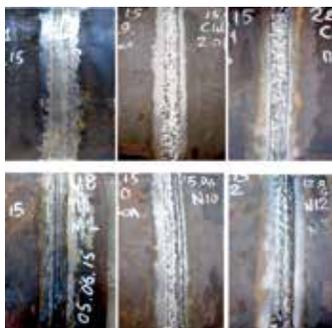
Вид стыковых (вверху) и нахлесточных (внизу) сварных соединений из трубной стали К60 толщиной 21,3 мм при механизированной подводной сварке порошковыми проволоками, слева-направо: ППС-АПЛ1, ППС-АПЛ2, ППС-АПЛ3
